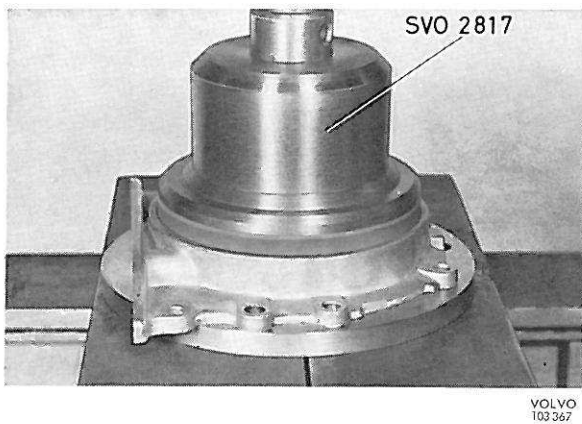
Montage du joint d'étanchéité (caoutchouc)
